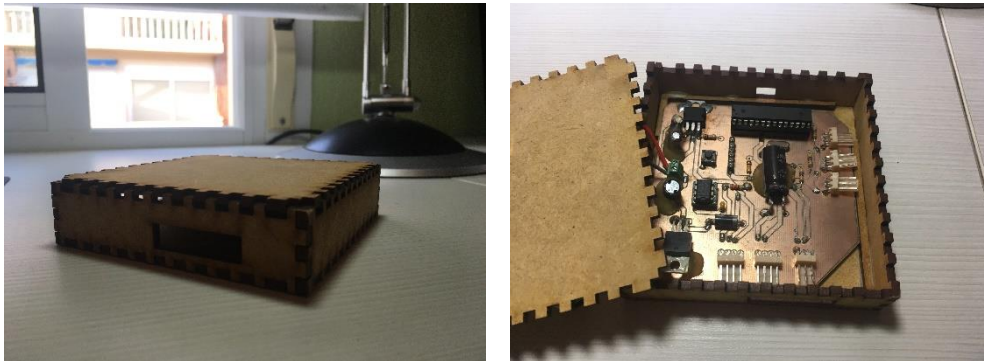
Caja de madera fabricada por el laboratorio de Etopia para introducir las placas
